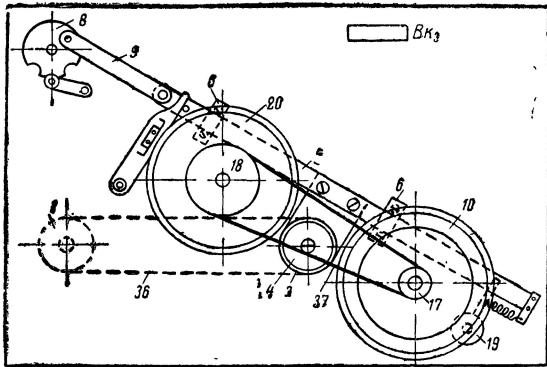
Расположение деталей на панели лентопротяжного механизма (вид снизу)
